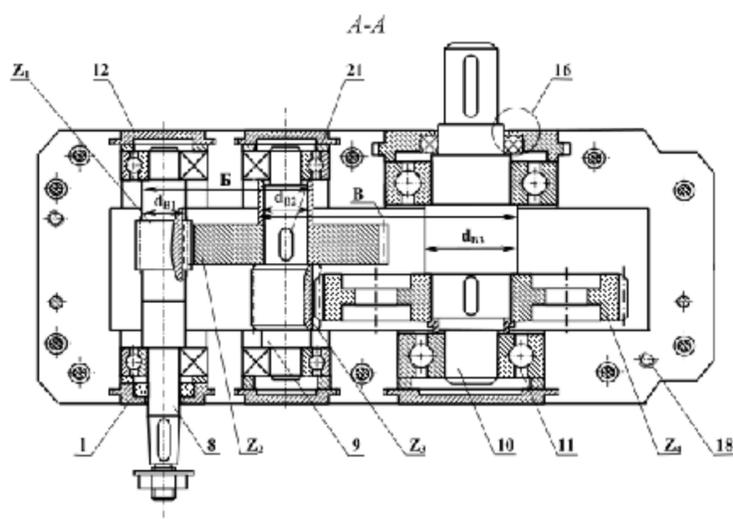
Конструкция редуктора с последовательным расположением валов
